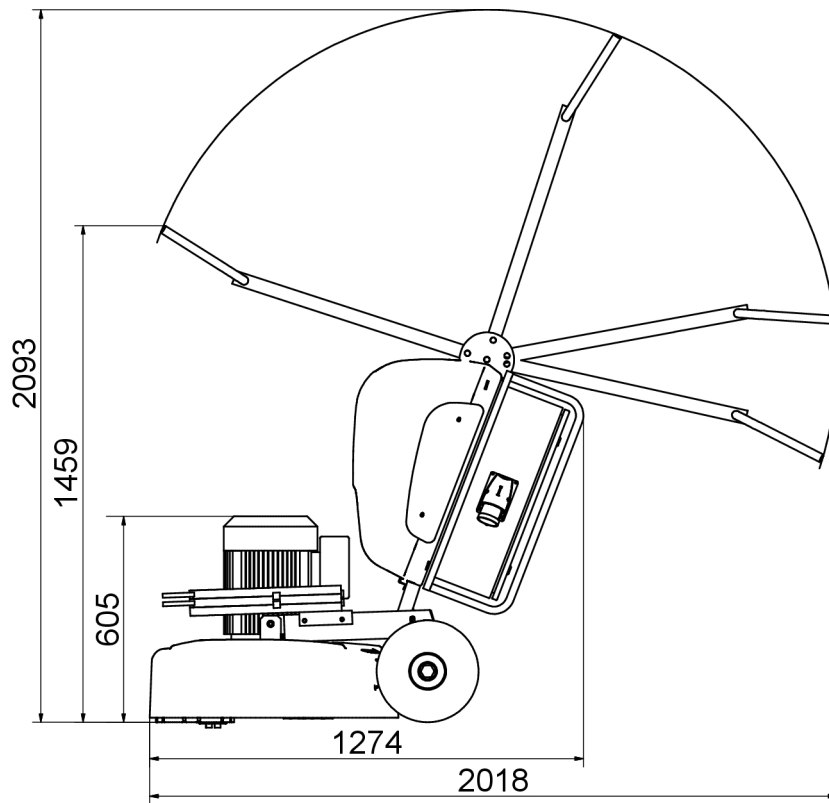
Maskinens höjd- och längdmått i millimeter
